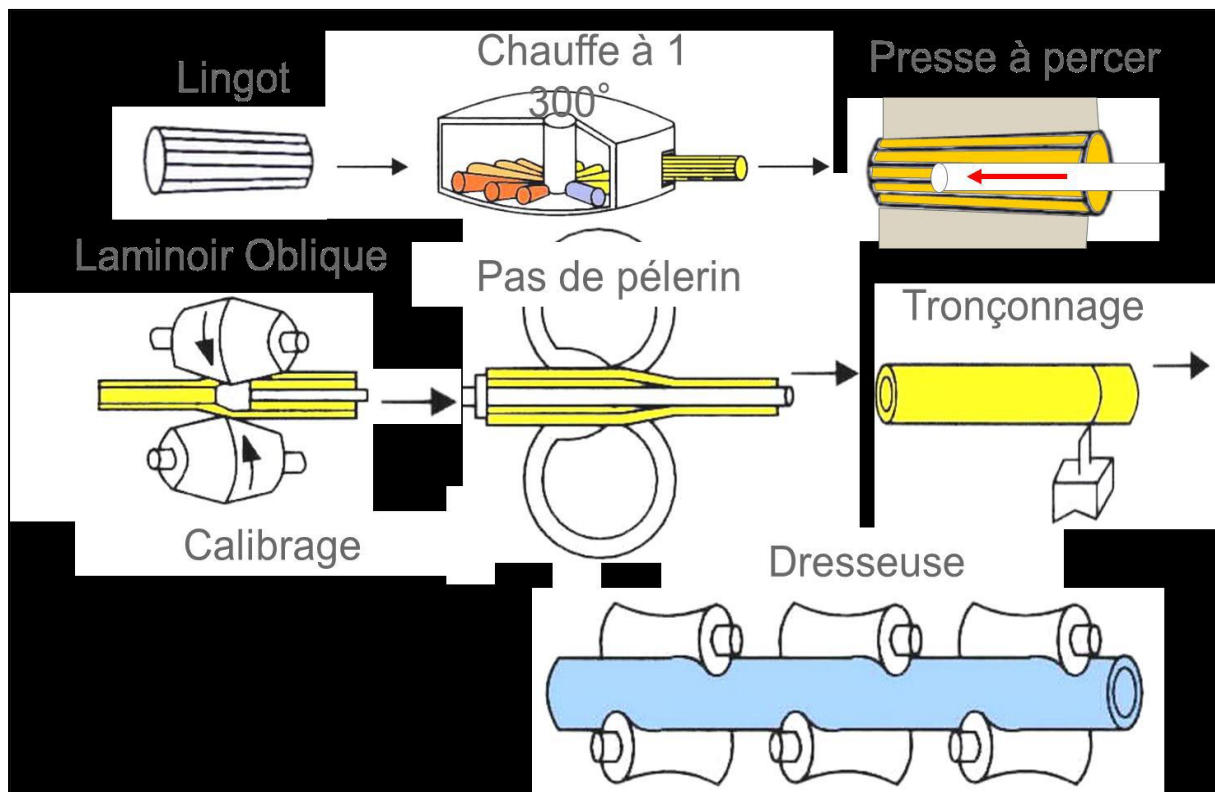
Processus de fabrication du tube sans soudure
